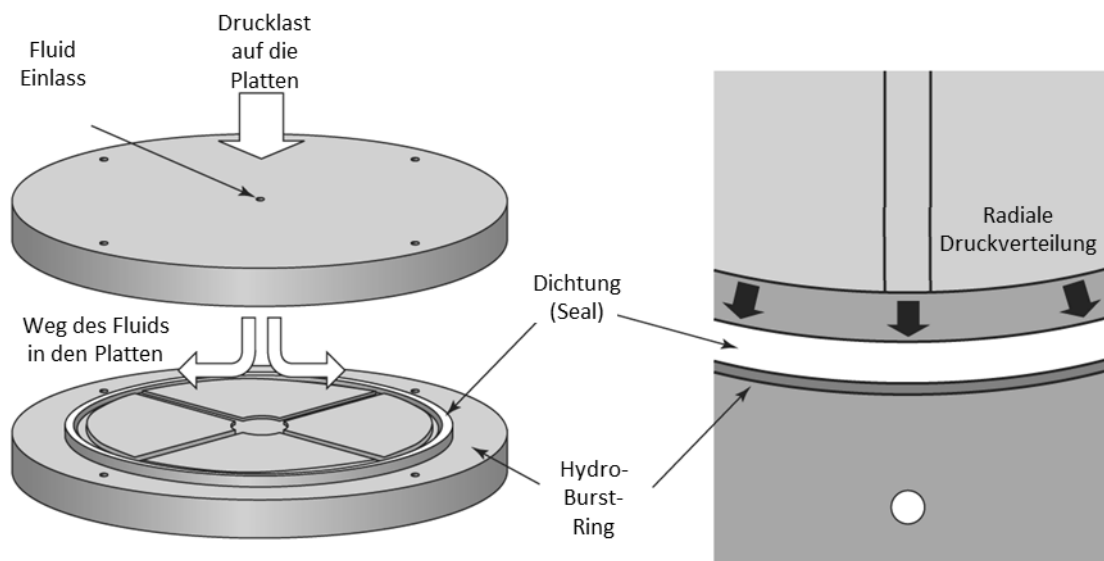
Prinzipieller Aufbau beim Hydro-Burst-Test
